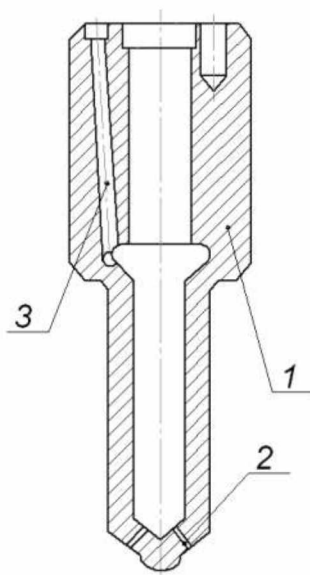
Корпус розпилювача: 1 – корпус; 2 – сопло розпилювача; 3 – паливний канал
